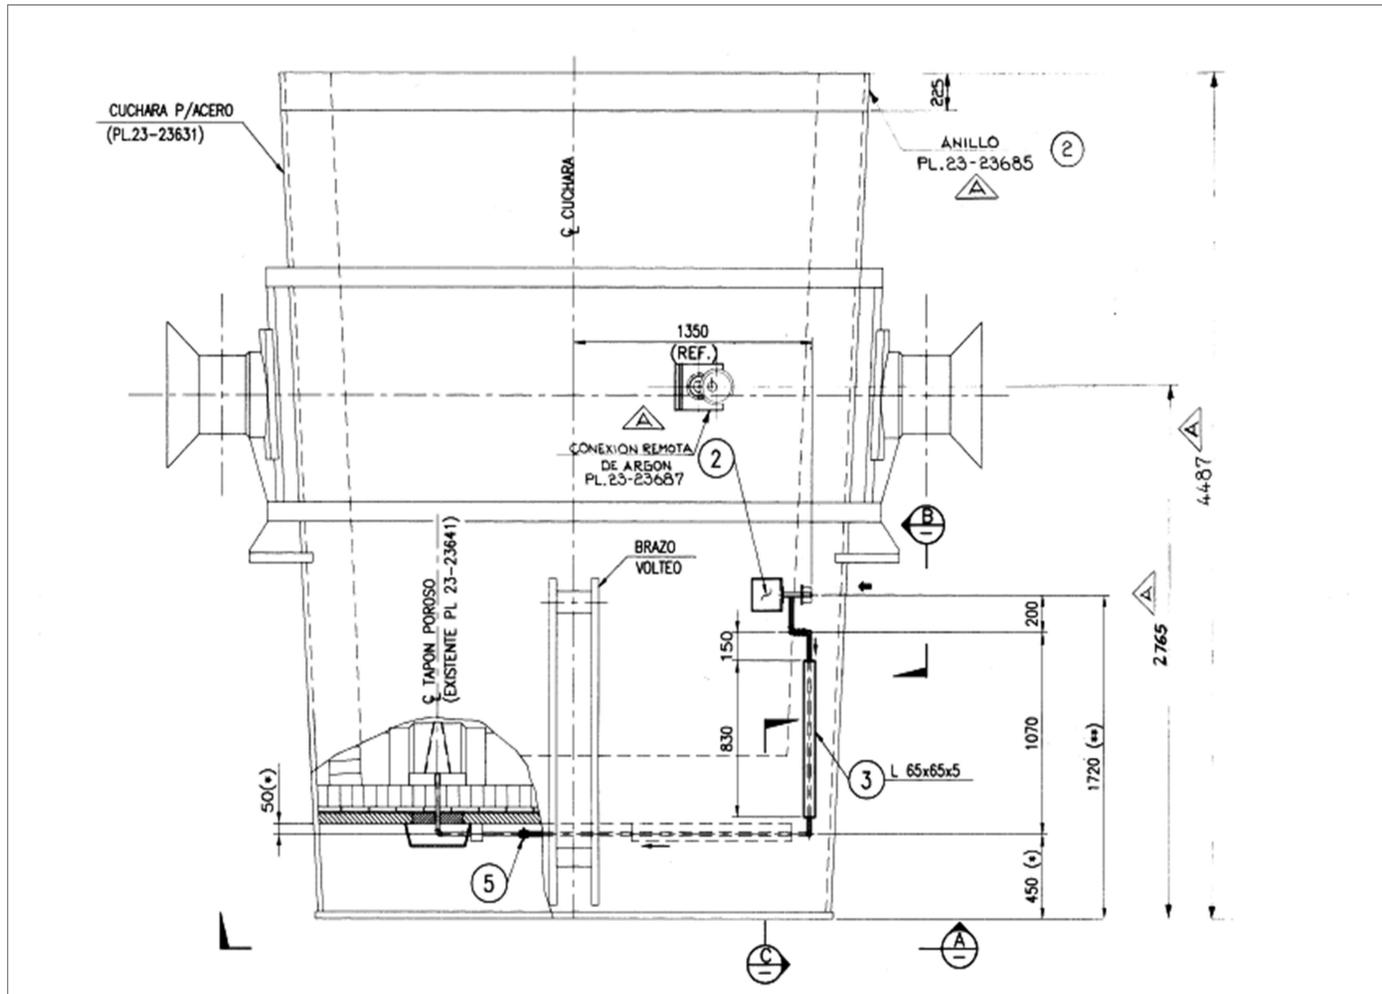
Detalles en plano de la Cuchara de Acero.
